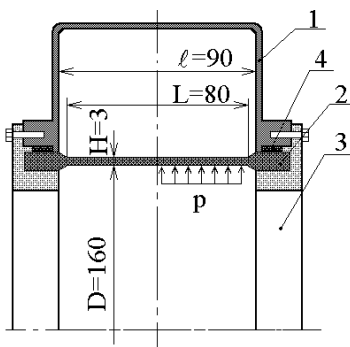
Цилиндрическая вакуумная камера с трубчатой стенкой из УУКМ
